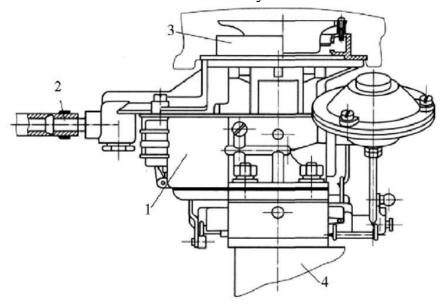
Газовый смеситель-насадка РЗАА на карбюраторе "Озон": 1 - корпус карбюратора; 2 - штуцер подвода бензина; 3 – насадка; 4 - впускной коллектор
